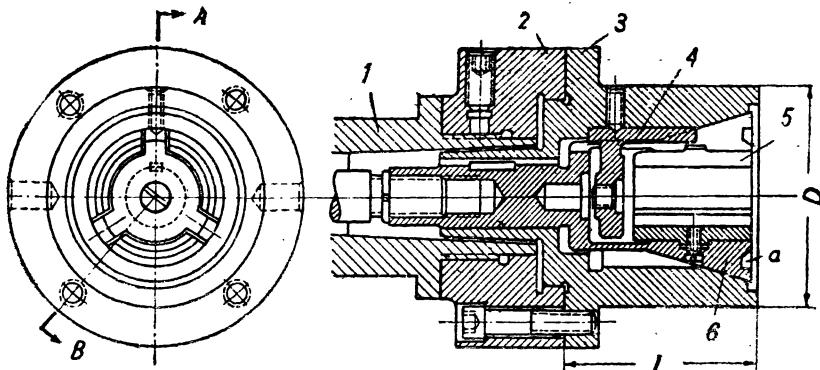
Универсальный цанговый патрон для вторичного зажима с затяжкой через шпиндель.
